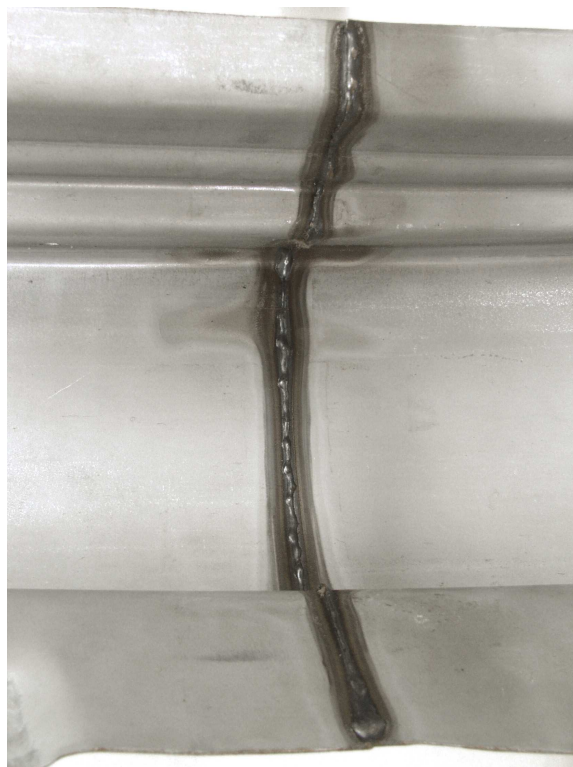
b): Detailaufnahme B-Säule mit Laserschweißnaht (ISAF, TU Clausthal)
